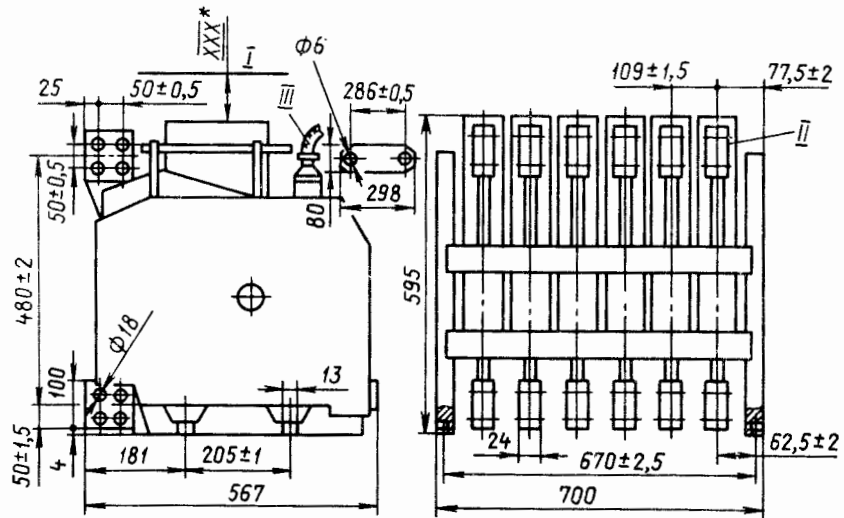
Габаритные и установочные размеры выключателей 3400 в двух- и трехполюсном исполнении:
